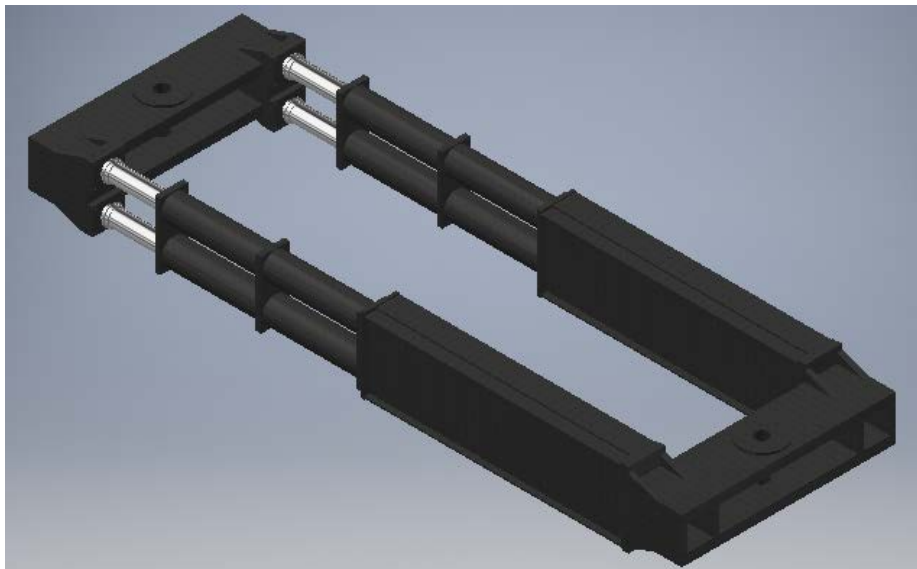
Vista isométrica máquina cabeçotes, pistões e vigas de 6 metros
